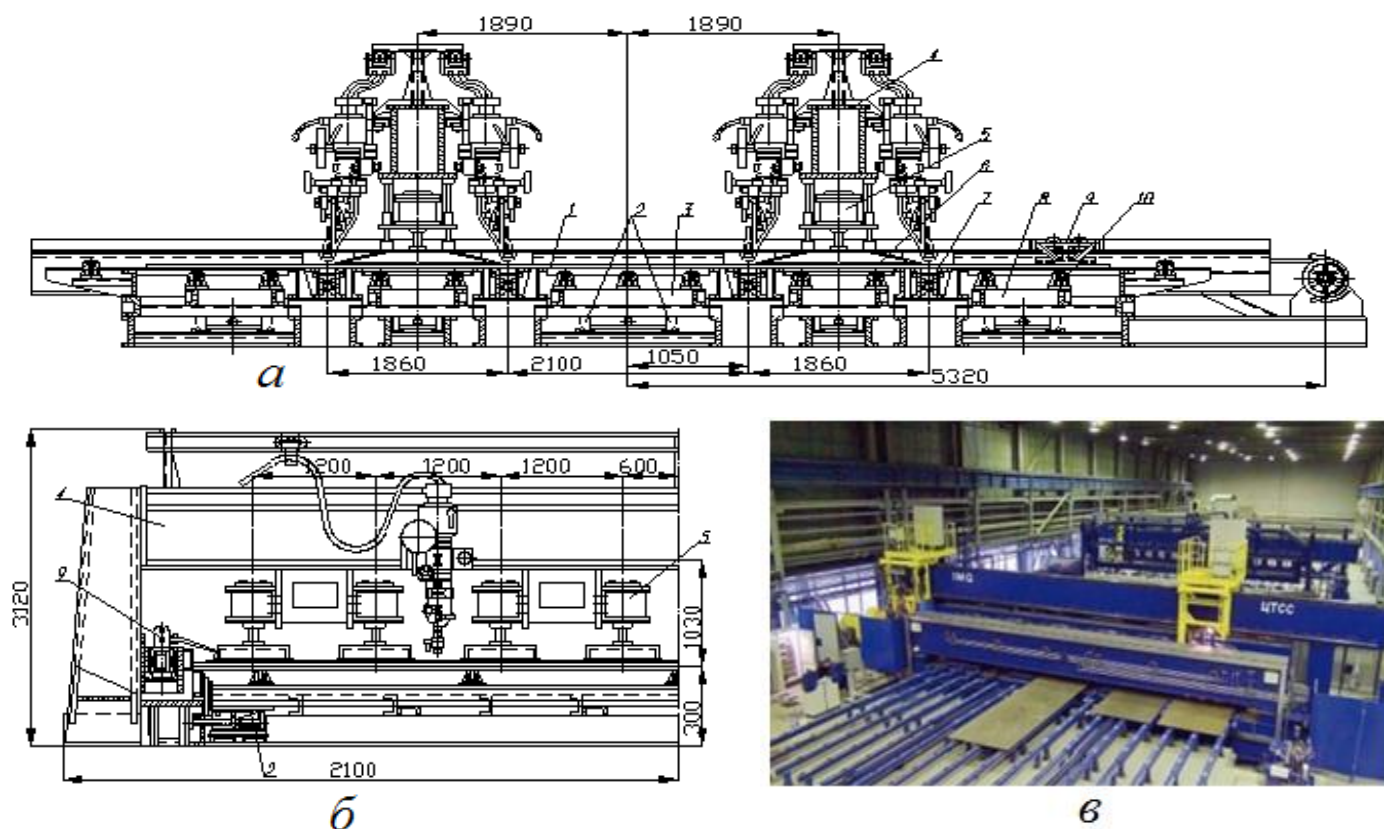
Установка зі стаціонарними флюсовими подушками для автоматичного зварювання полотнищ:
